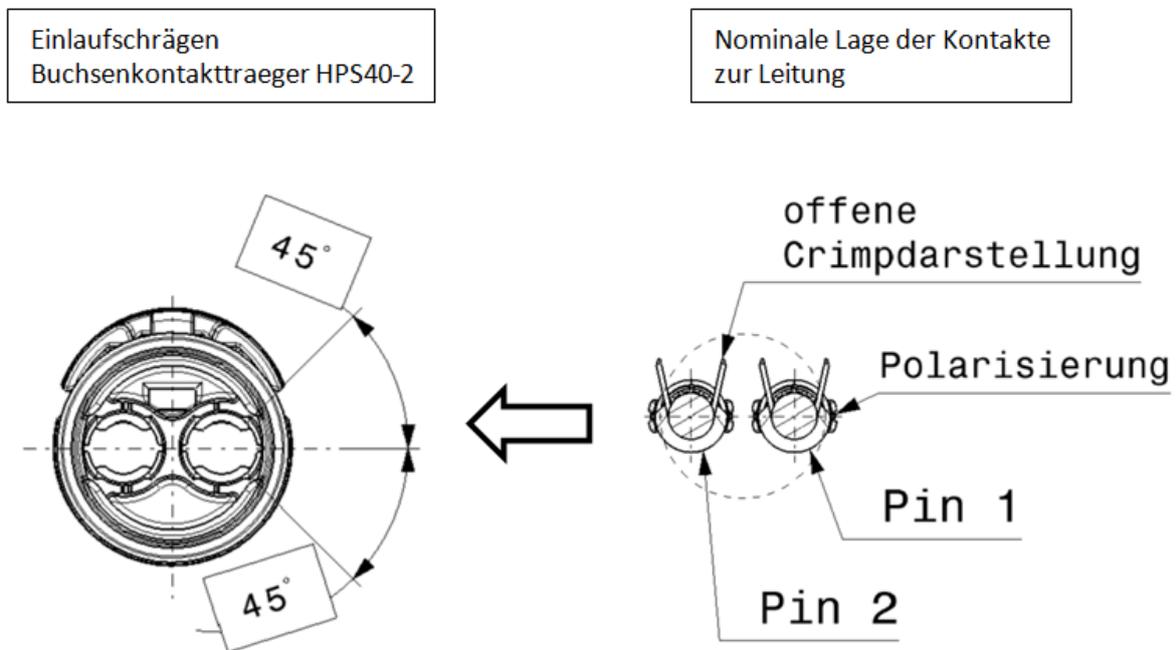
Geometrie der Einlaufschrägen am Buchsenkontakträger
